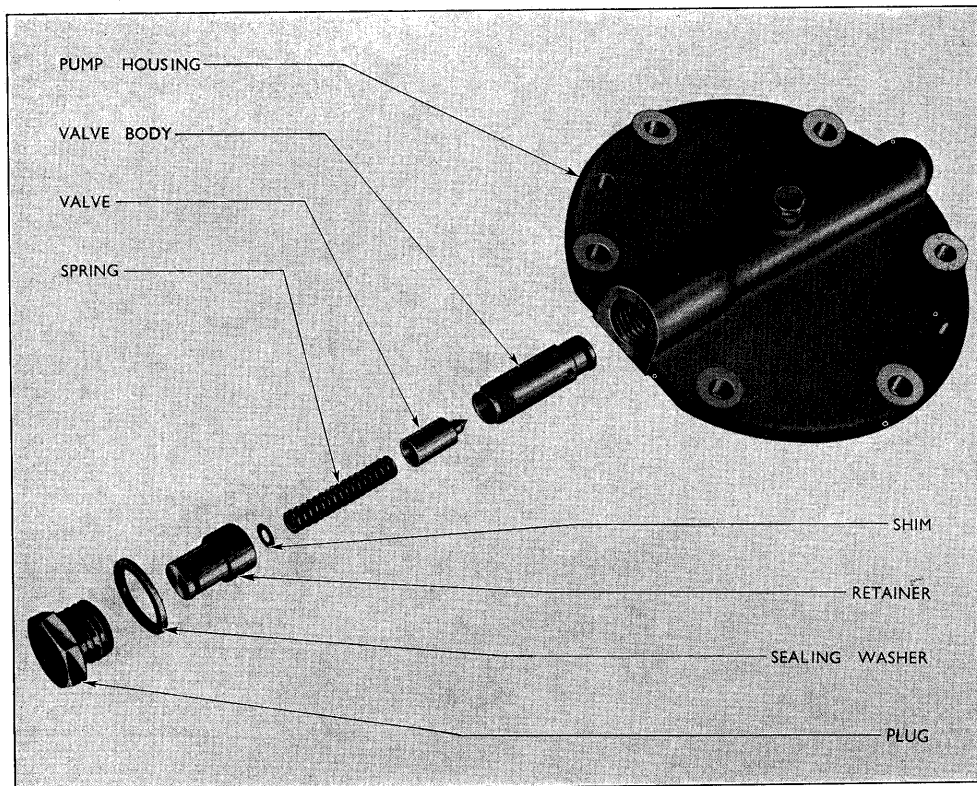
Hydraulikpumpens sikkerhedsventil.
